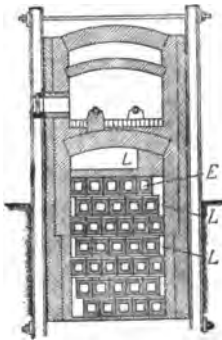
Rekuperator der Iföfenbaugesellschaft in Berlin, eingebaut in einen Stoßofen mit Weardalefeuerung. Der Rekuperator besteht aus hohlen, dünnwandigen, viereckigen Schamottsteinen, die oben und unten Rippen besitzen. Diese Rippen bilden die Luftkanäle, während die Hohlsteine den Essengasen Durchgang gewähren. Letztere ziehen senkrecht zur Luft hindurch. Die Luft zieht in Schlangenwindungen von unten nach oben. Die dünnwandigen Steine lassen die Wärme leicht hindurchtreten, sodaß man bis zu 70% der Abgaswärme gewinnen kann. Der Stoßofen leistet 75 t in 24 Stunden bei Qualitätsstahlblöcken mit 8% Kohle (7000 WE) und 1% Abbrand. Stahl und Eisen, 1914, S. 276.
